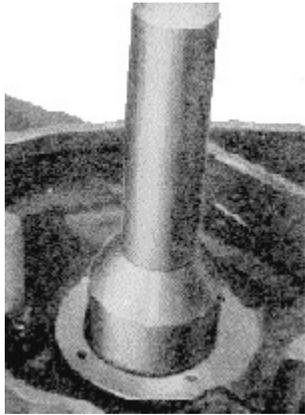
Einsetzen des Ringrillenslagers 6303 mit dem Dorn 05 MW 11-4
